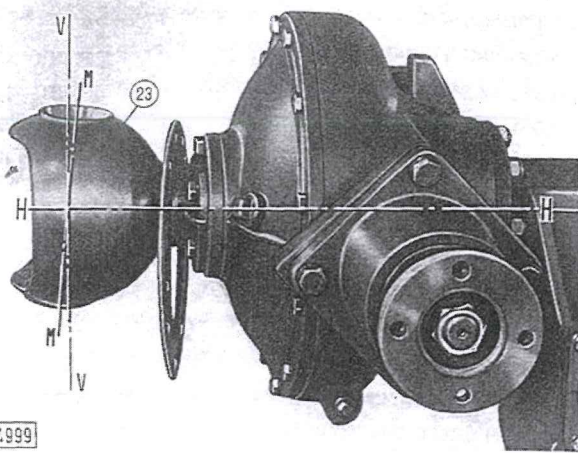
Montaggio corretto del supporto sferico (23).
